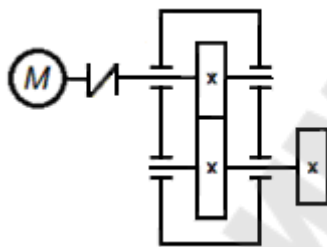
Кинематическая схема привода с открытой цилиндрической передачей
